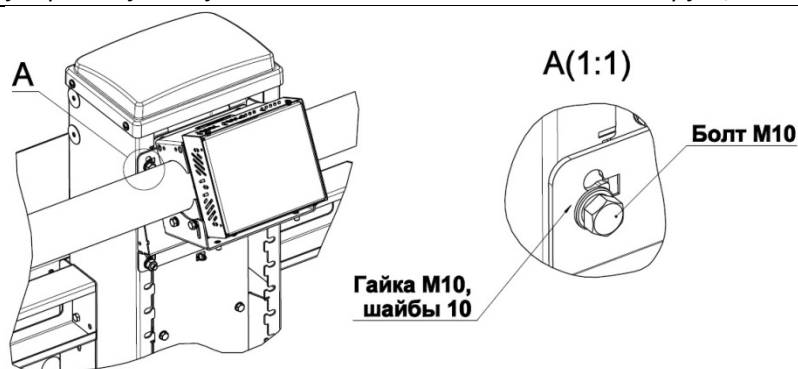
Установка и закрепление балки на колонну без привода
